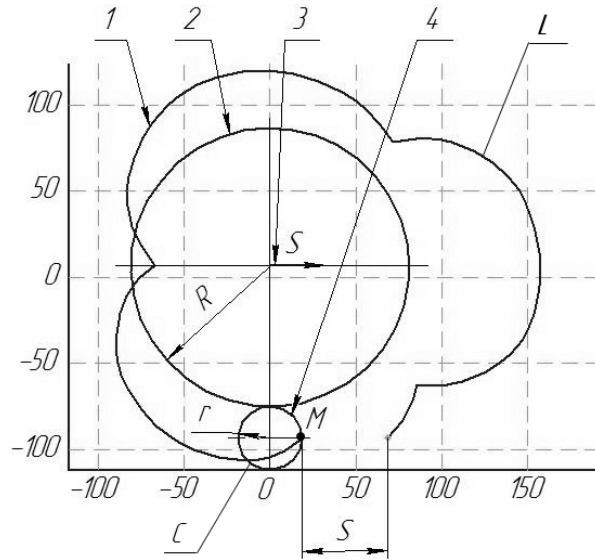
Траєкторія відносного руху вершини ножа і обробленої поверхні
